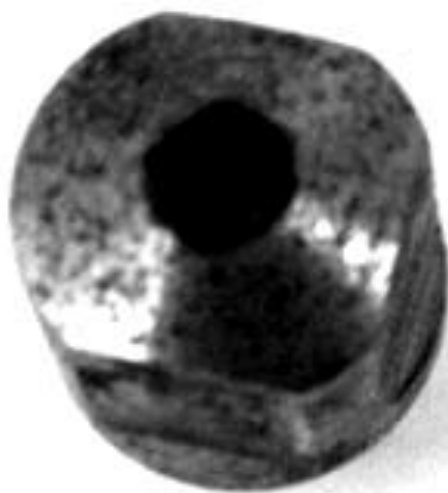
Фото инструмента с разрушенной рабочей вставкой
